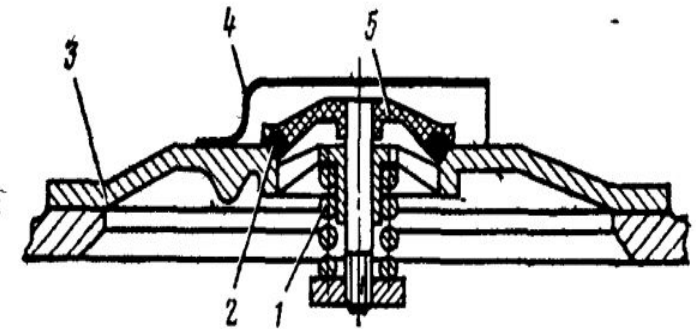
Схема предохранительного клапана двигателя ЧСП18/22
